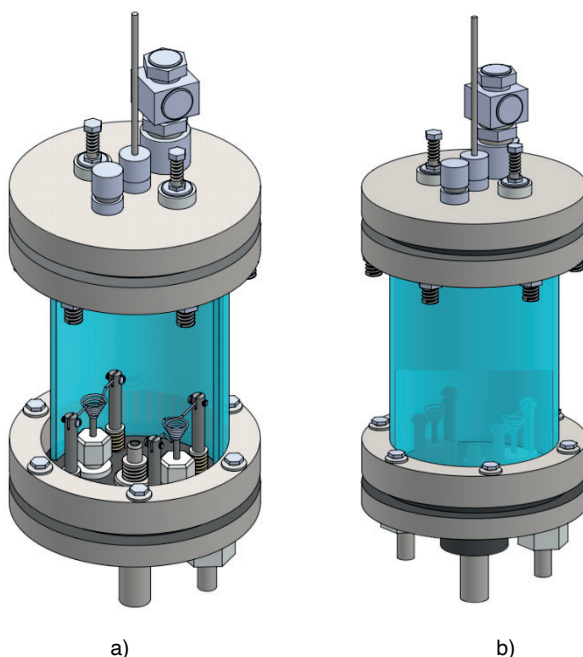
Ensamble final del reactor CVD: a) vista isométrica con componentes internos visibles, b) vista externa del sistema totalmente ensamblado.
